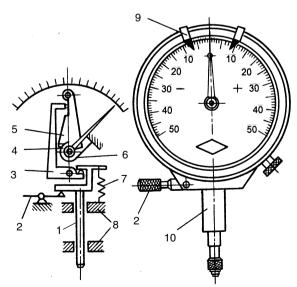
Рычажно-зубчатая измерительная головка 1ИГ:
